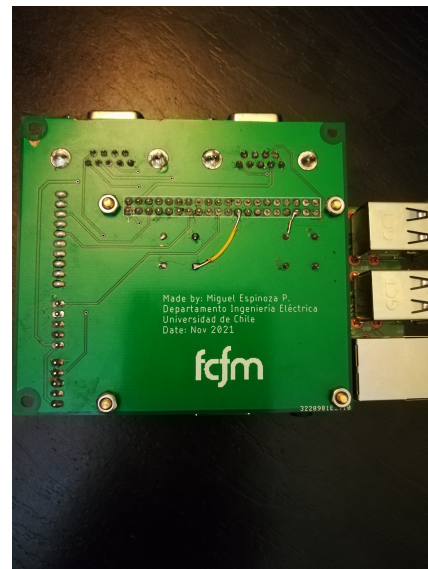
Lado inferior de la placa PCB del módulo central.
